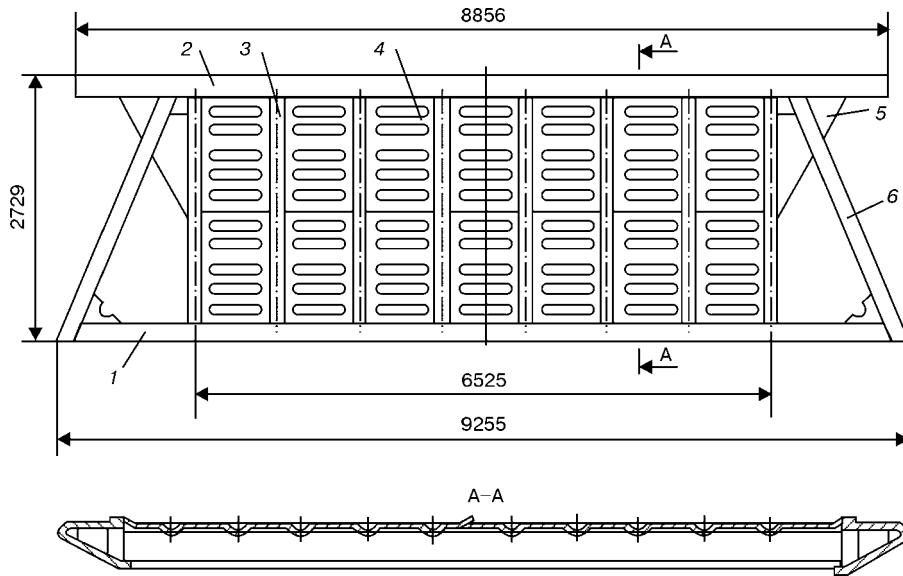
Общий вид боковой стены вагона-минераловоза: 1 — обвязка нижняя; 2 — обвязка верхняя; 3 — стойка; 4 — лист обшивки; 5 — лист крайний; 6 — раскос
